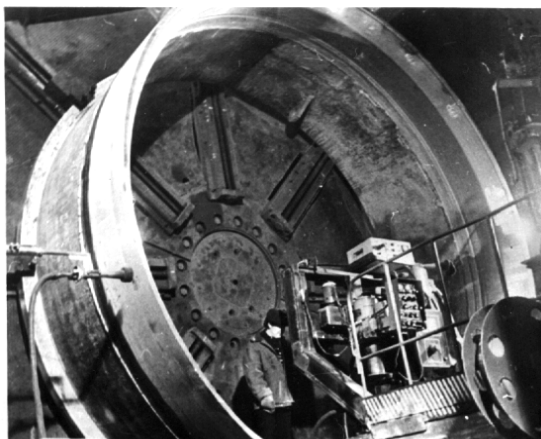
Общий вид установки для сварки с программированием режима чаш засыпных аппаратов
